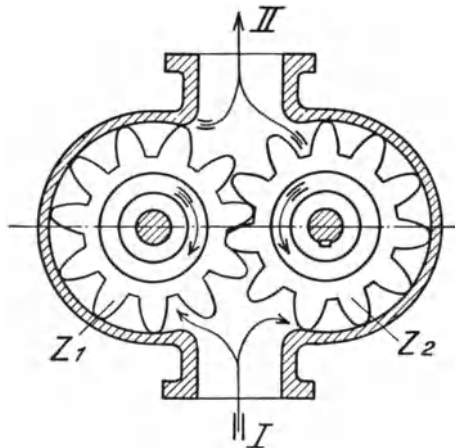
Zahnradpumpe, Z_1 Z_2 Zahnräder
